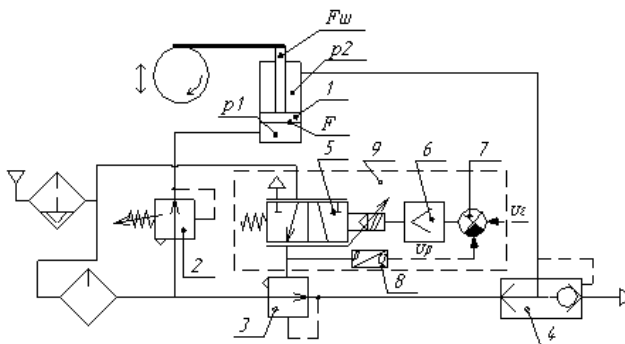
Пневматична система керування циліндром шліфувальної бабки з використанням аналогового електропневматичного перетворювача
